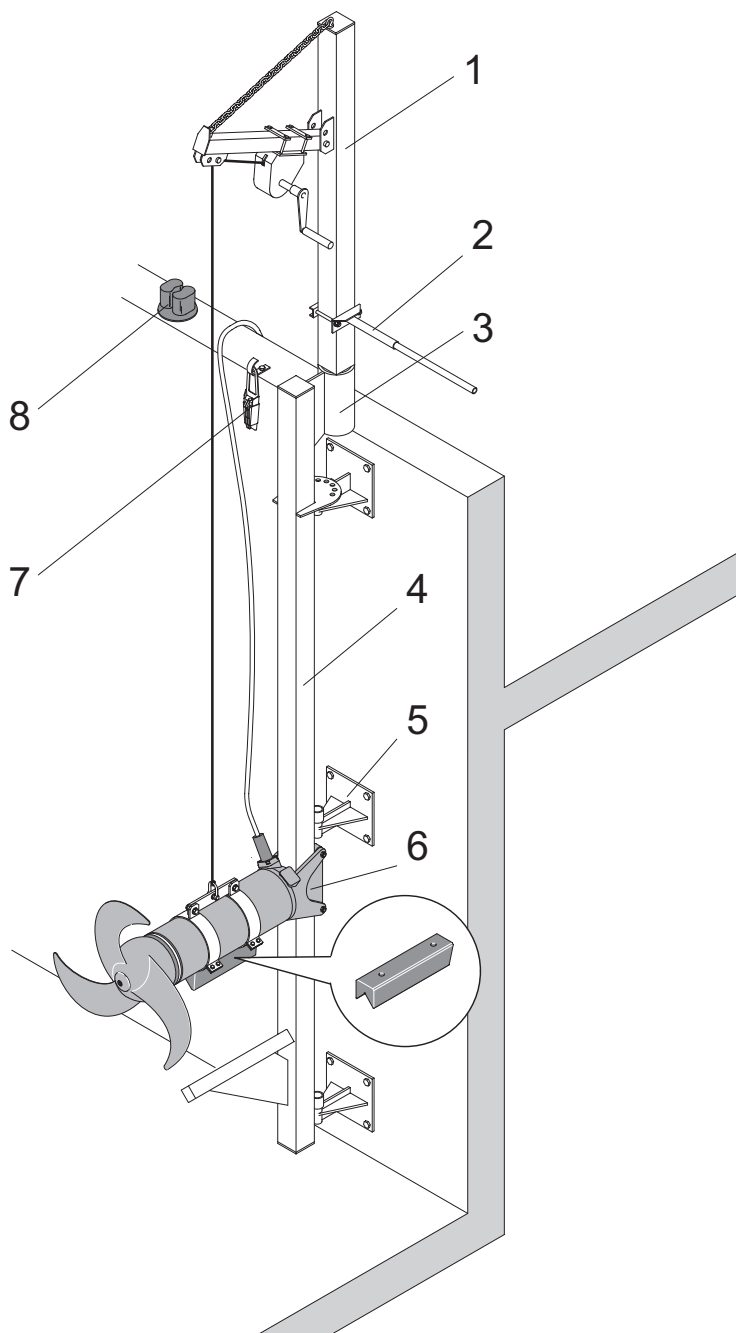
Exemple d'installation avec d'autres possibilités de fixation
